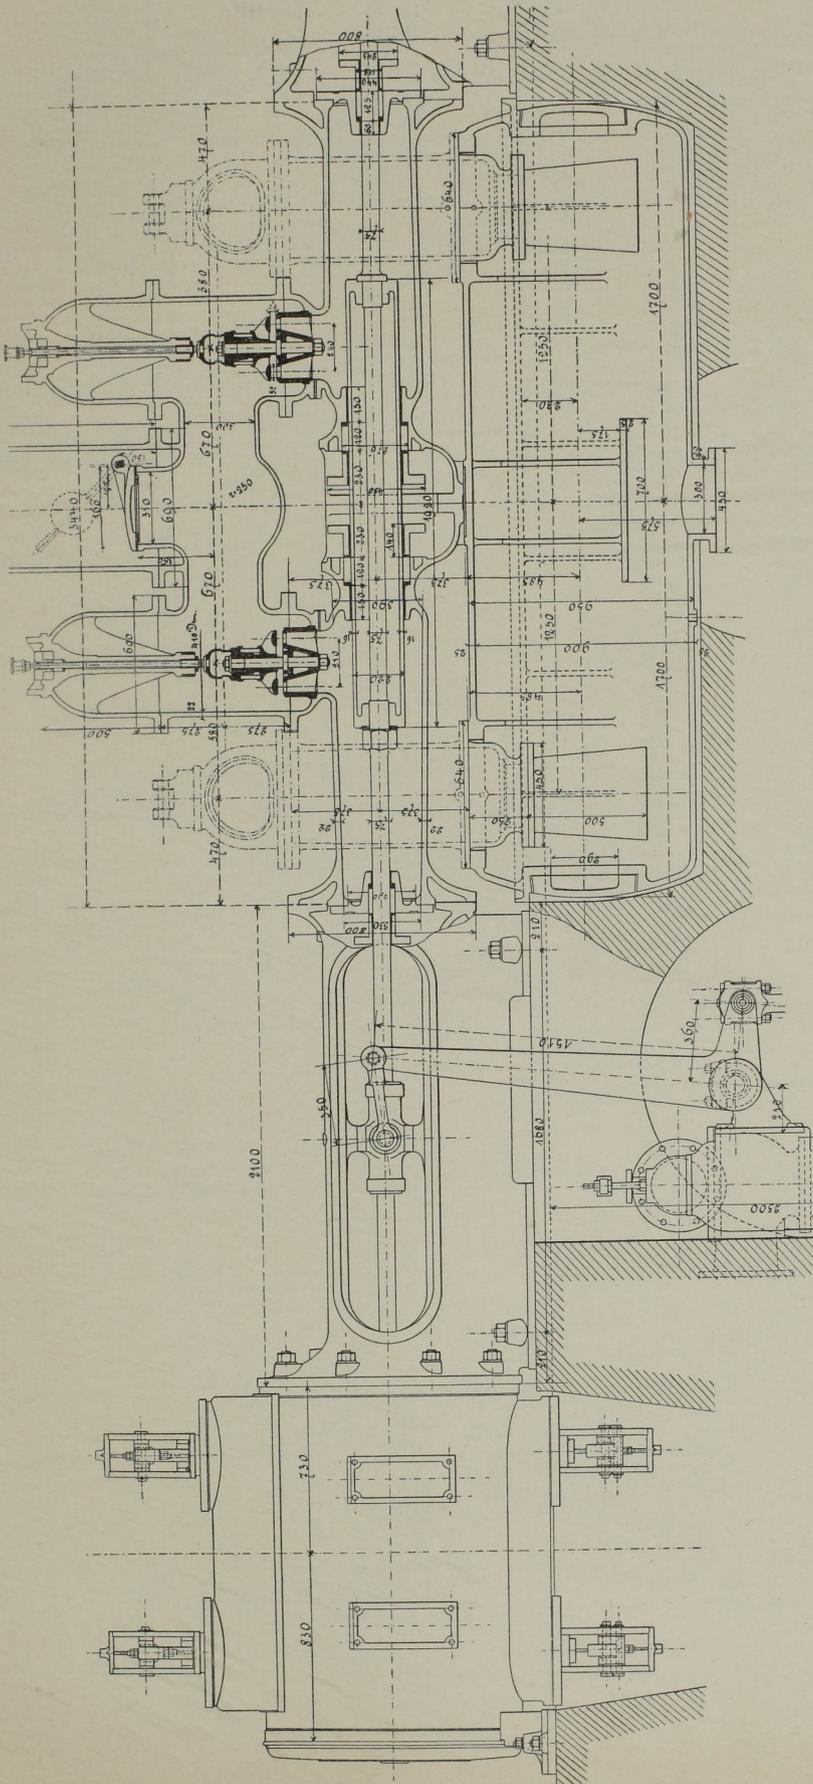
Seitenansicht und Längsschnitt der Druckpumpe.
